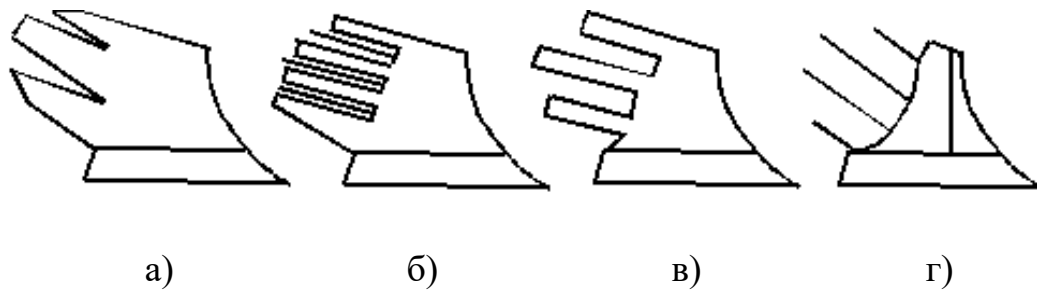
Корпуса с различными отвальными поверхностями а - щелевой; б - полосовой с прутками; в - пластинчатый; г - прутковой
